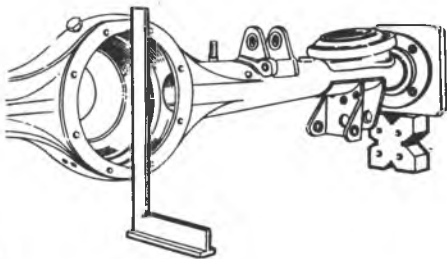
Проверка перпендикулярности поверхности крепления редуктора
